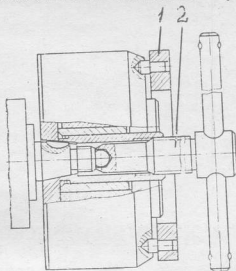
Снятие муфты приспособлением И-801.16.000:
